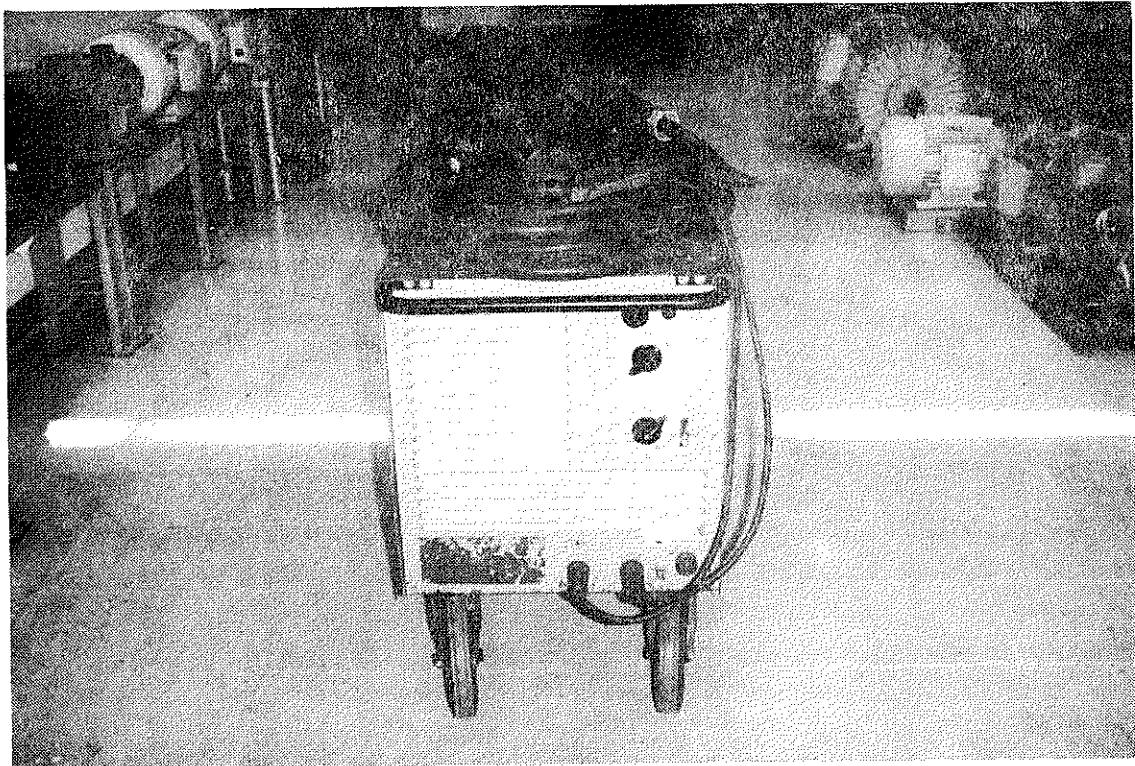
Equipo de soldadura para electrodo revestido.
